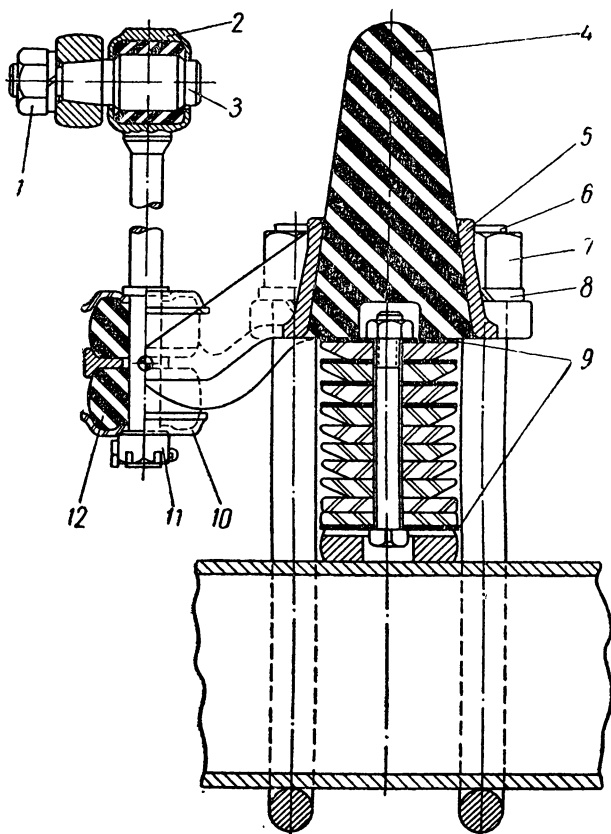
Крепление заднего конца передней рессоры автомобиля М-72:
